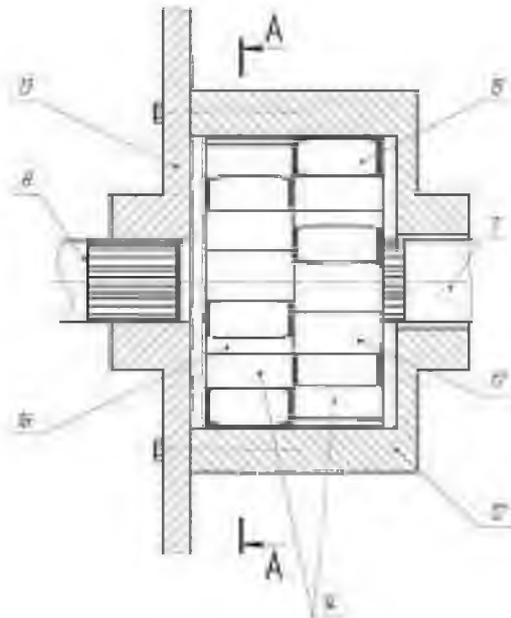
Схема предлагаемой конструкции дифференциала (разрез)
